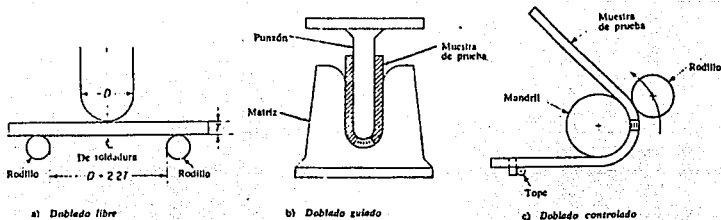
Diferentes pruebas de doblado efectuadas para elementos soldados.
